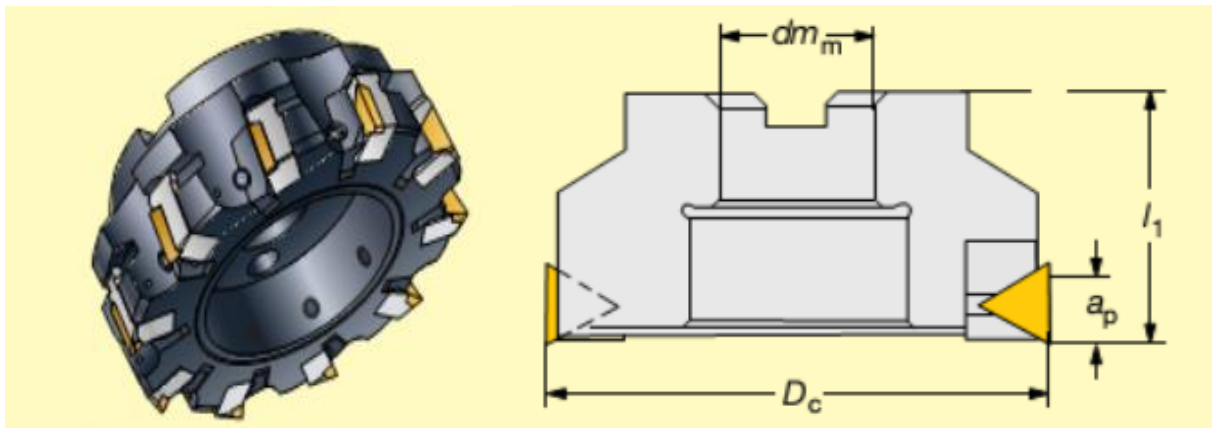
Фреза торцева ModullMill[33]
